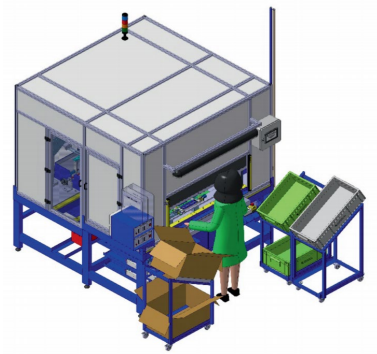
Equipamento de soldadura por ultrassom e puncionar terminais [39]
